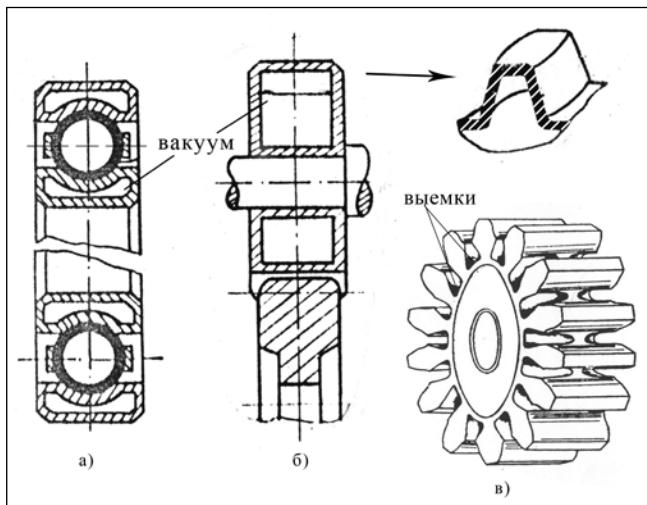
Упругие узлы и детали: а) полый подшипник, б) полое зубчатое колесо, в) зубчатое колесо с выемками у ножек зубьев
